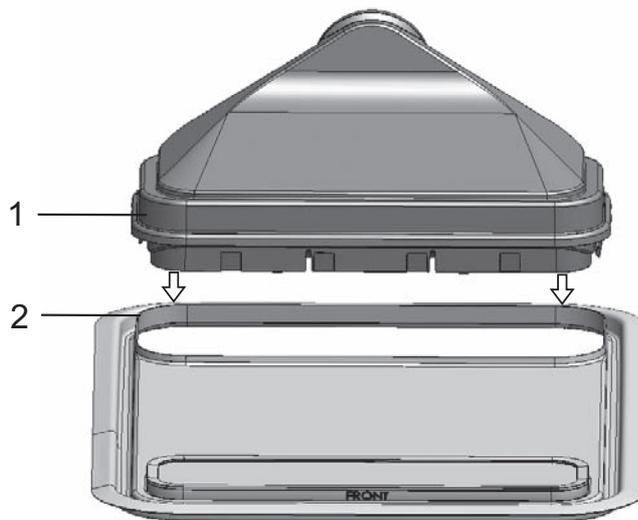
Montage du boîtier du filtre à air sur le couvercle du réservoir d'eau
